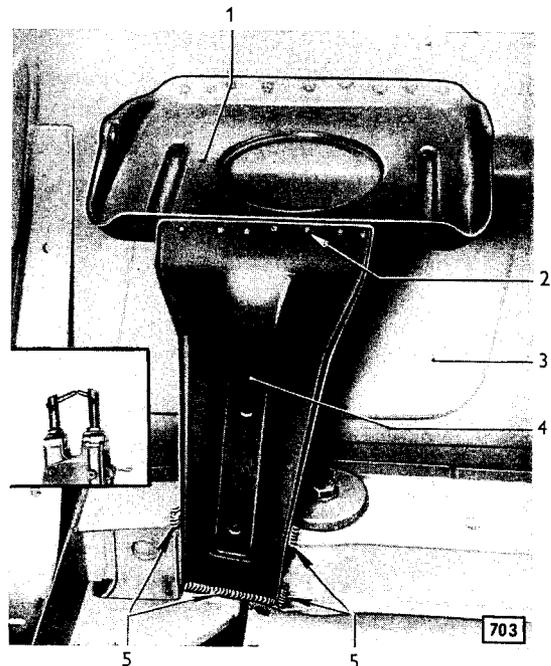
Stütze an Batteriehälter punktschweißt und an Vorderrahmenlängsträger lichtbogengeschweißt
